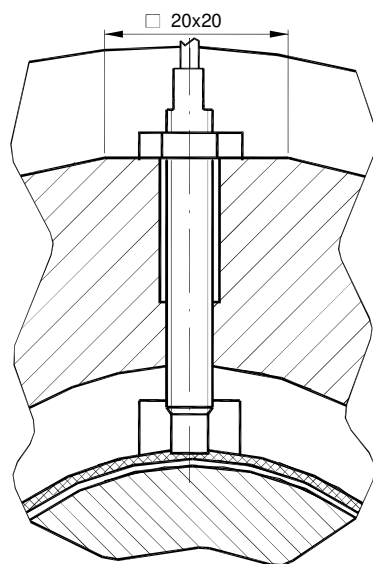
Установка датчика ES400.010, IES400.010 в корпусе подшипника
